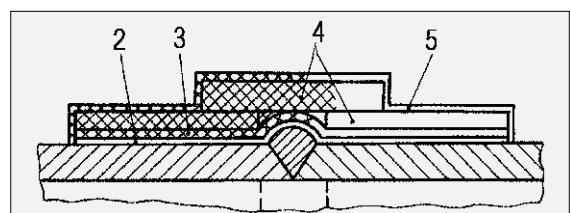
Ремонт или усиление стыкового сварного шва (обозначения см. рис. 1)
